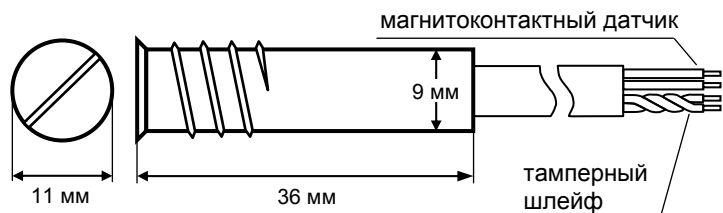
Геркон извещателя К-3 2Е в металлическом корпусе
